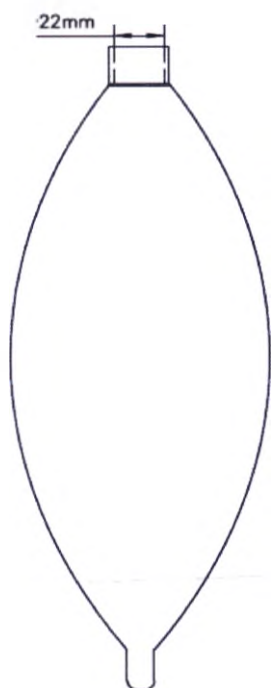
Мешок резервуарный для дыхательного контура
